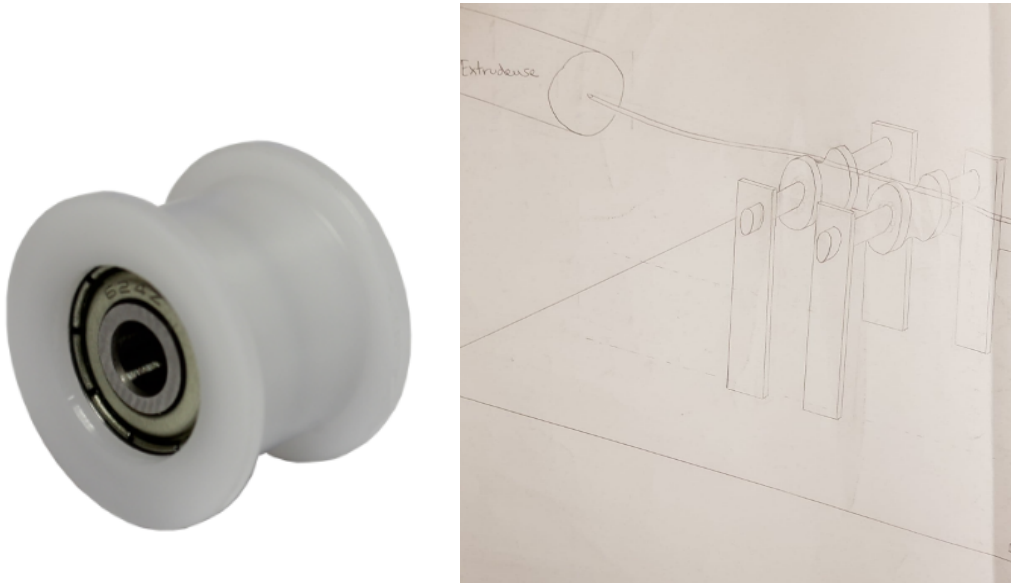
Poulie roue libre et Dessin du sous ensemble
